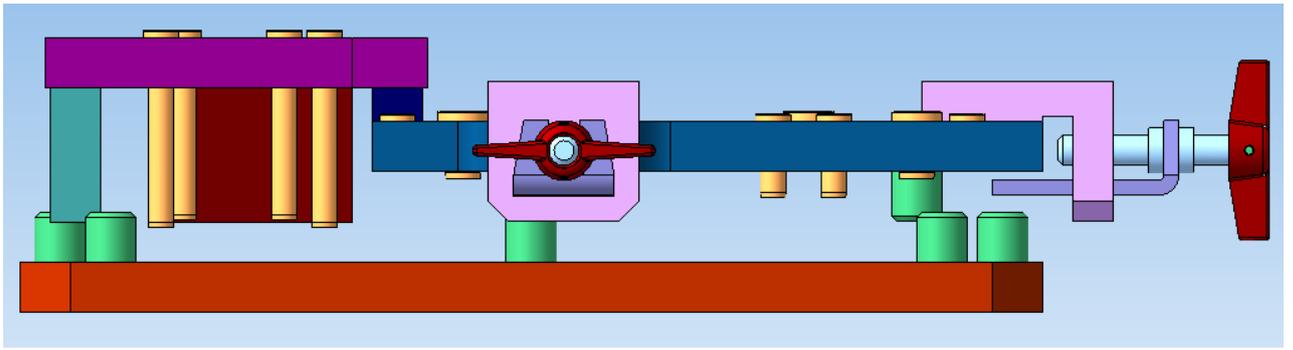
Трехмерная модель зажимного приспособления (вид сбоку)
